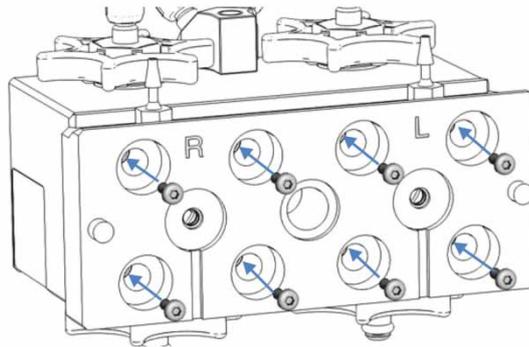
Pumpenkopf mit Hinterspülplatte und Schrauben für die Platte
